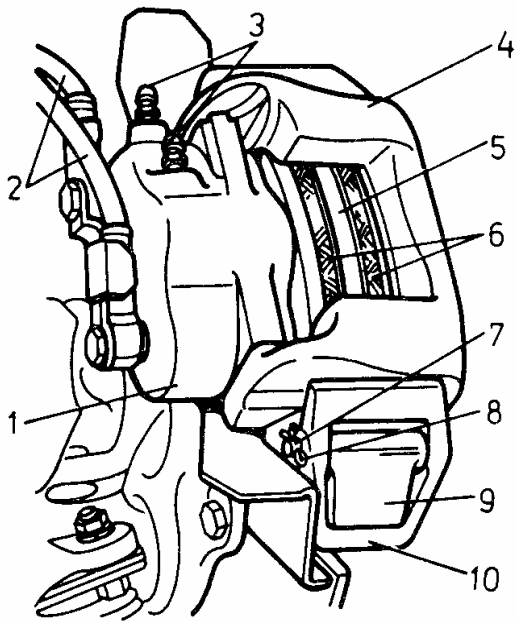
Freno delantero: 1 - bloque de cilindros; 2- mangueras flexibles; 3- racores; 4- soporte; 5- disco de freno; 6- zapatas (pastillas) de freno; 7- eje de la palanca de presión; 8- pasador hendido; 9- guía de las pastillas; 10- palanca de presión
